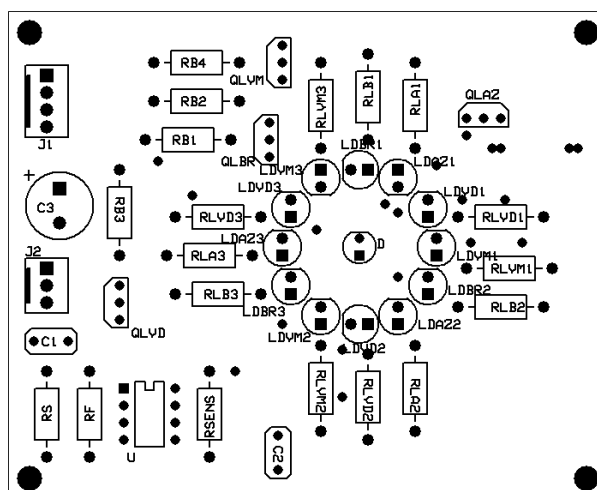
Vista do topo da montagem da placa de circuito impresso.
